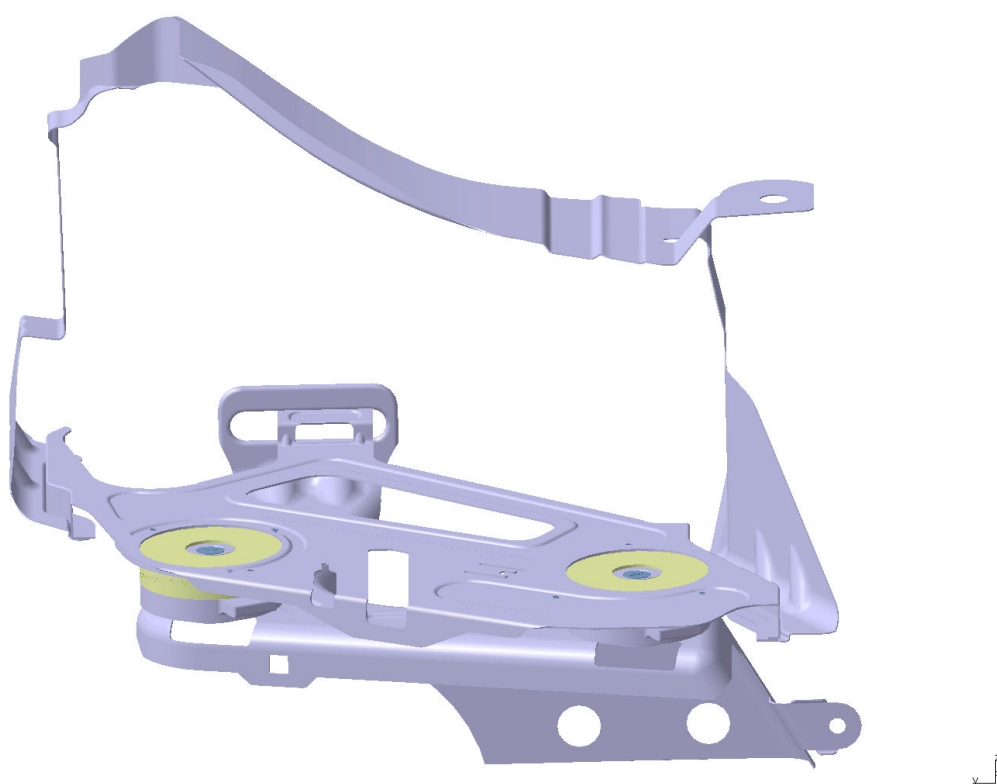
Držák 7 s okolními díly. Pohled zepředu.
